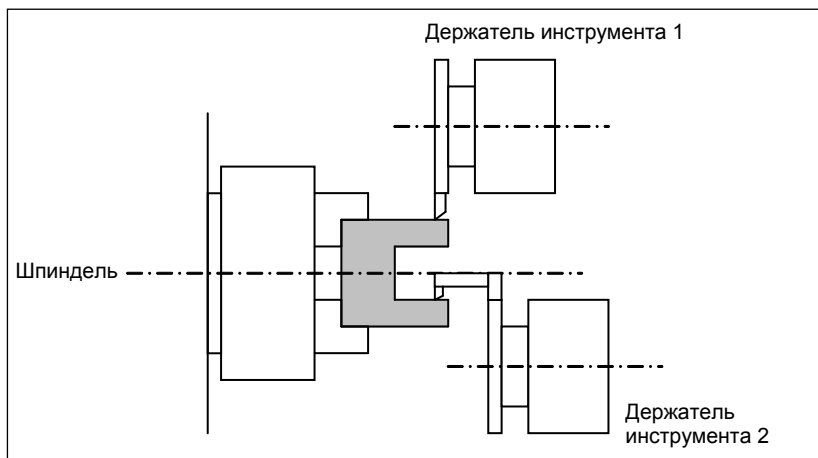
(а) Применение на станке с одним шпинделем и двумя резцедержателями
